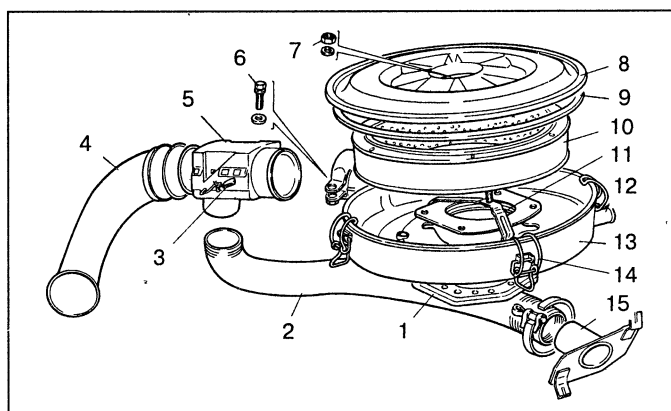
Воздушный фильтр и терморегулятор: 1 – уплотнительная прокладка; 2 – гофрированный шланг; 3 – рукоятка заслонки терморегулятора; 4 – заборник холодного воздуха; 5 – терморегулятор; 6 – стяжной болт; 7 – гайка крепления крышки фильтра; 8 – крышка воздушного фильтра; 9 – уплотнитель крышки фильтра; 10 – фильтрующий элемент; 11 – кронштейн крепления крышки фильтра; 12 – вытяжной коллектор картерных газов; 13 – корпус воздушного фильтра; 14 – пружинный держатель; 15 – заборник подогретого воздуха из зоны выпускного коллектора
